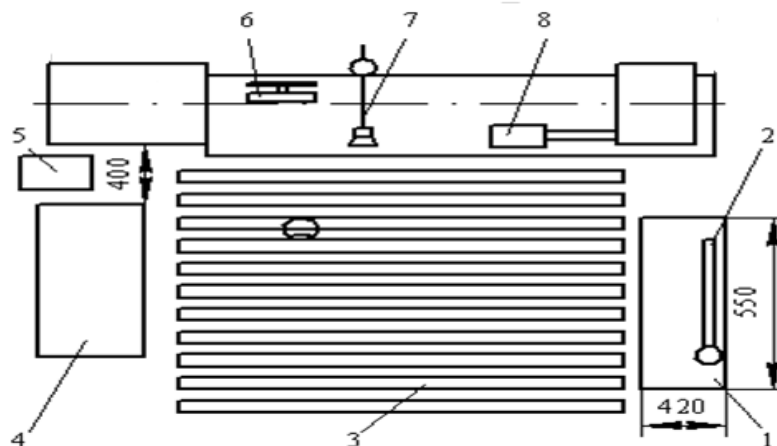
Планировка рабочего места оператора при обработке деталей в патроне: 1 – инструментальная тумбочка; 2 – планшет для технологических карт; 3 – решётка под ноги; 4 – стеллаж для деталей; 5 – урна для мусора; 6 – защитный экран; 7 – лампа местного освещения; 8 – планшет для измерительного инструмент
